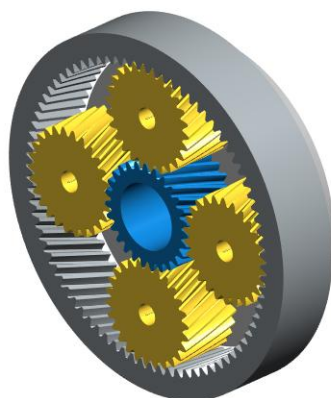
1º estágio; Engrenagens planetárias a amarelo; Engrenagem solar a Azul; engrenagem anelar a cinzento
